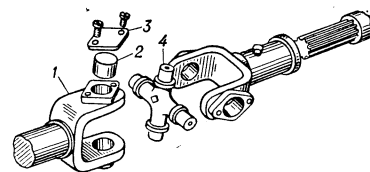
Полный кардан: 1 — вилка; 2 — опора для цапф крестовины; 3 — крышка; 4 — крестовина.
